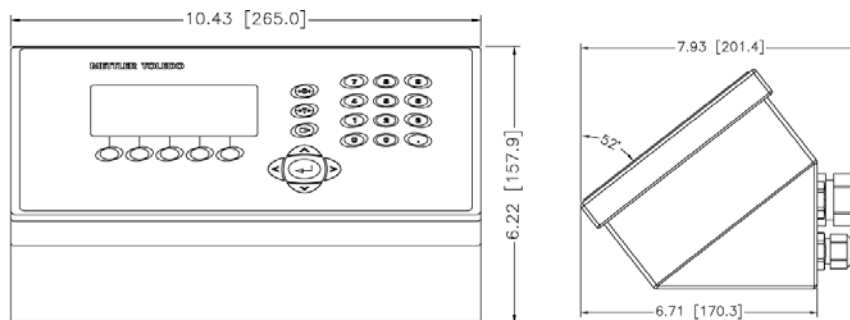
Dimensiones de la caja tipo montaje en panel del IND560 PDX
